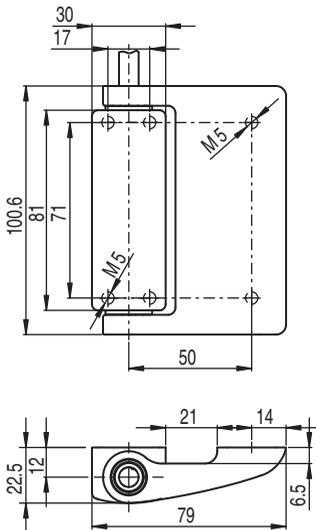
Dimensões do S410-M1CB2-T em mm
